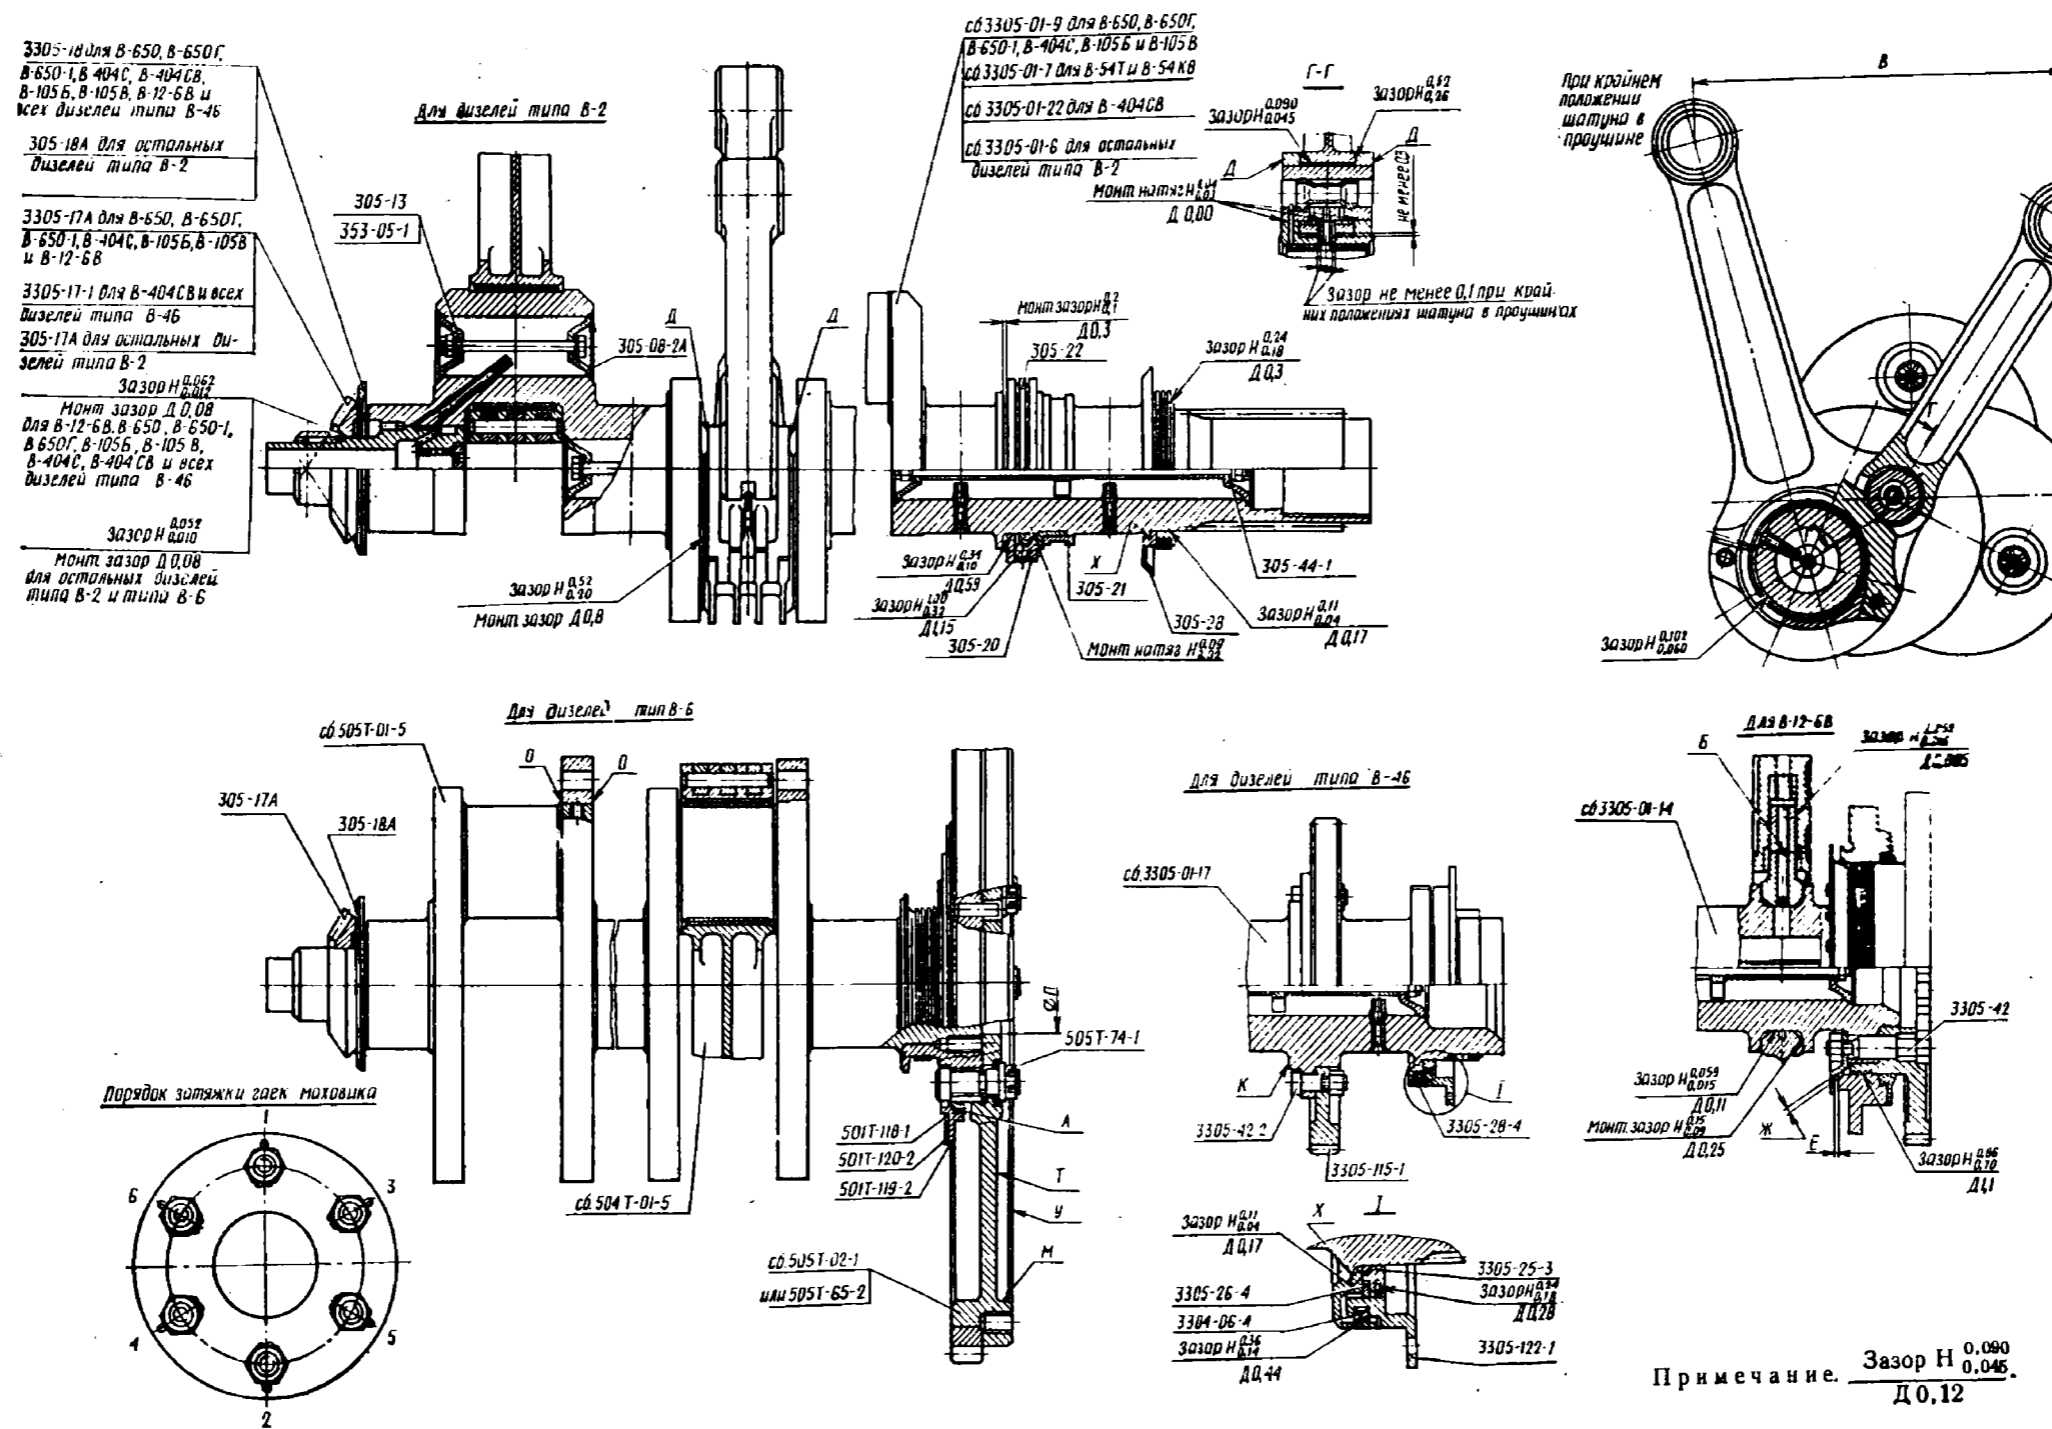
Коленчатый вал в сборе для дизелей типа В-2, типа В-46 и типа В-6:
